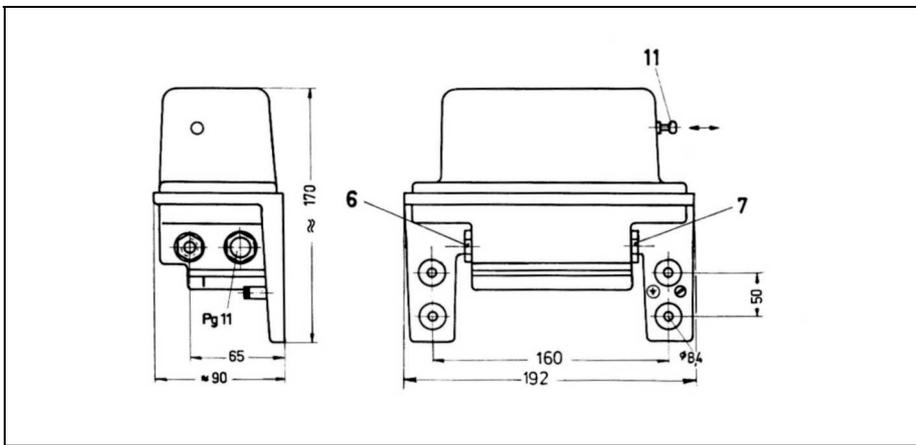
Maßskizze der Membranpumpe 2 (Maße in mm)
